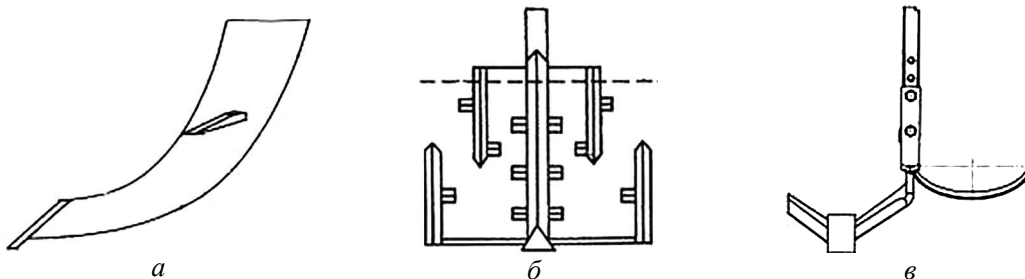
Тип стоек глубокорыхлителей с плоскими режущими (а), серповидными (б) и кольцевыми режущими (в) элементами
